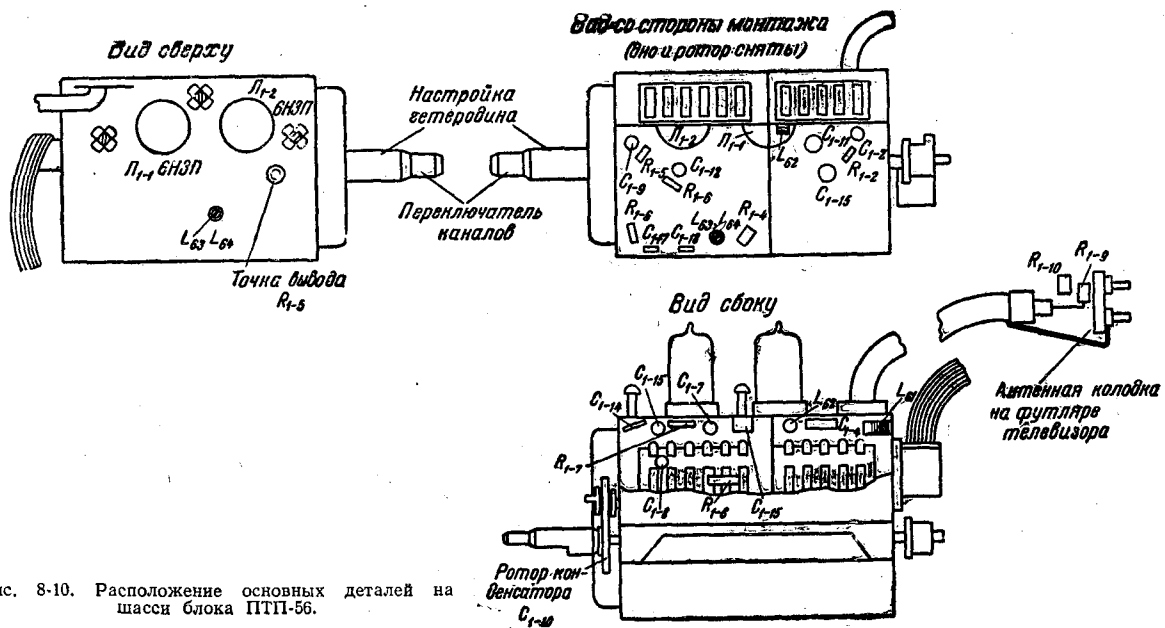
Расположение основных деталей на шасси блока ПТП-56.
